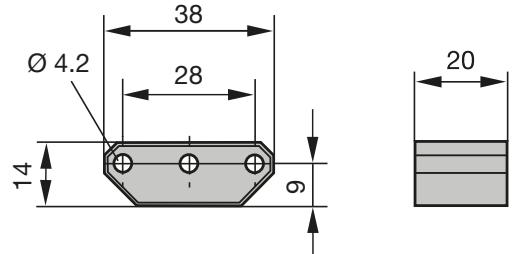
Einbaumaße Positionsgeber BTL5-P-3800-2
